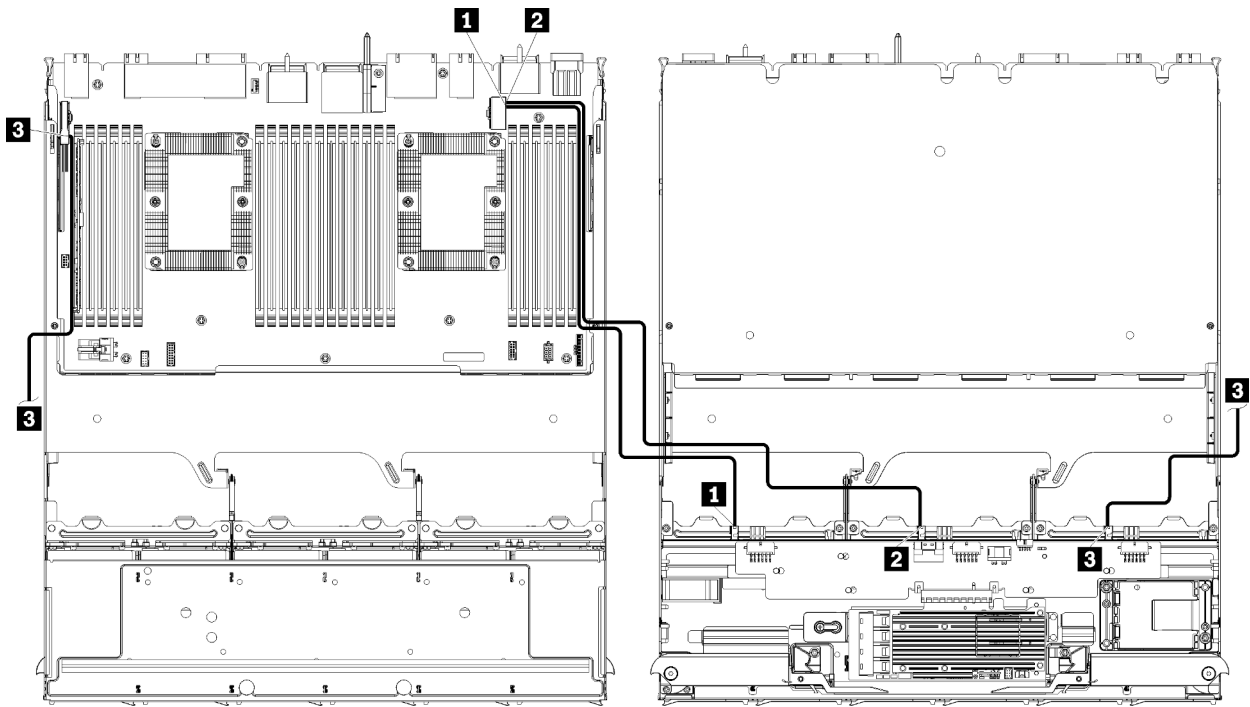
Disposición de los cables, cables de unidad SAS (bandeja superior con conjunto de placa de almacenamiento)
